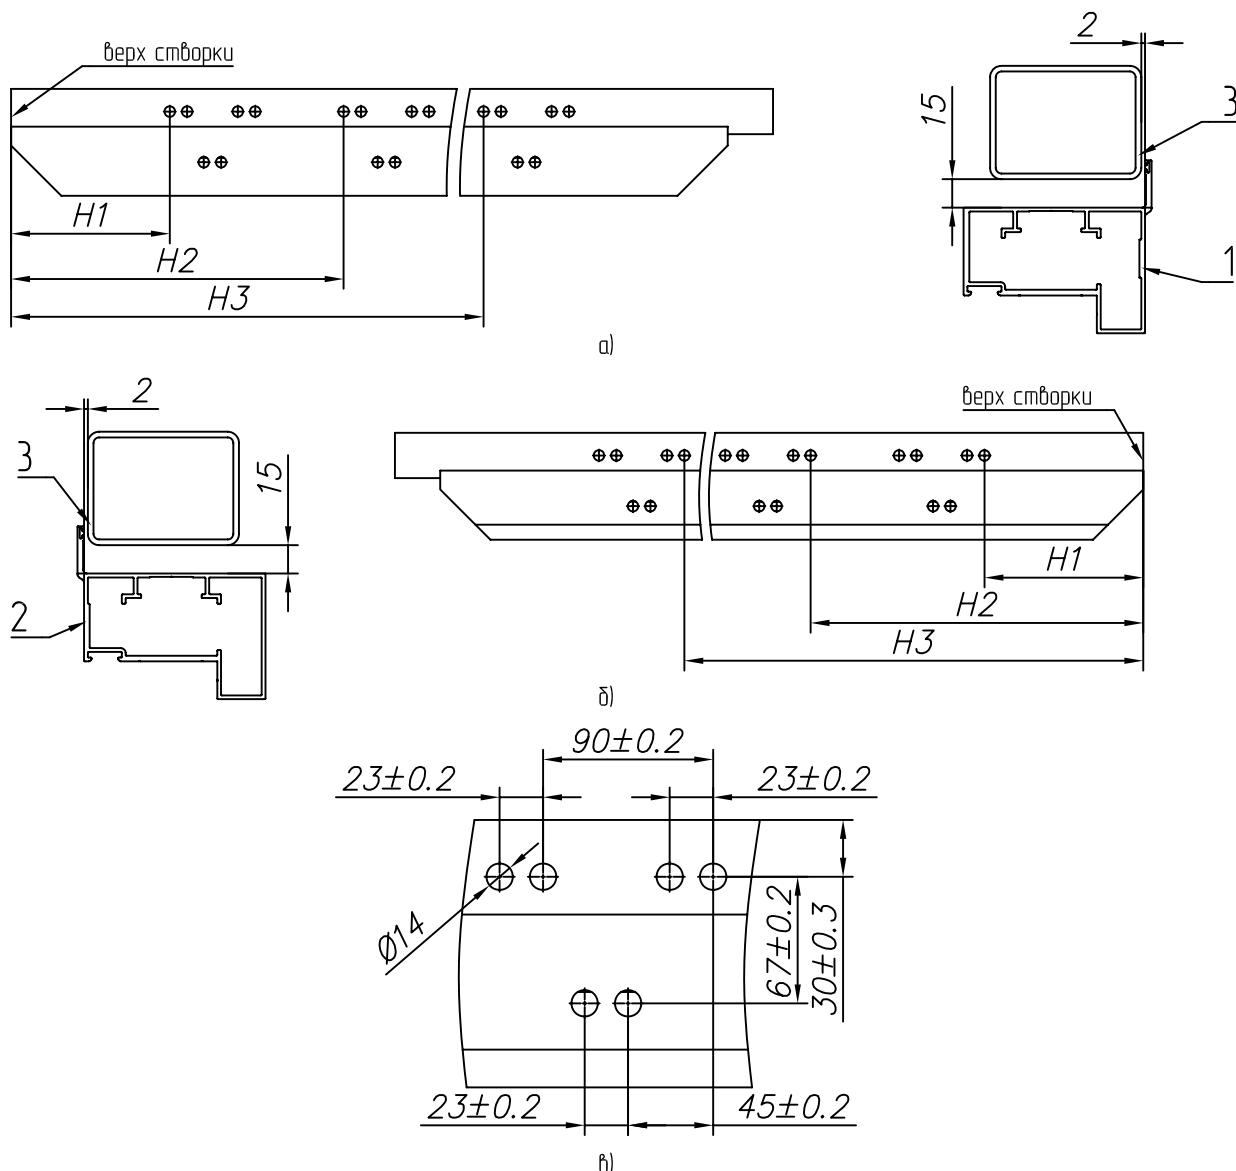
Изготовление групп отверстий для крепления петель
